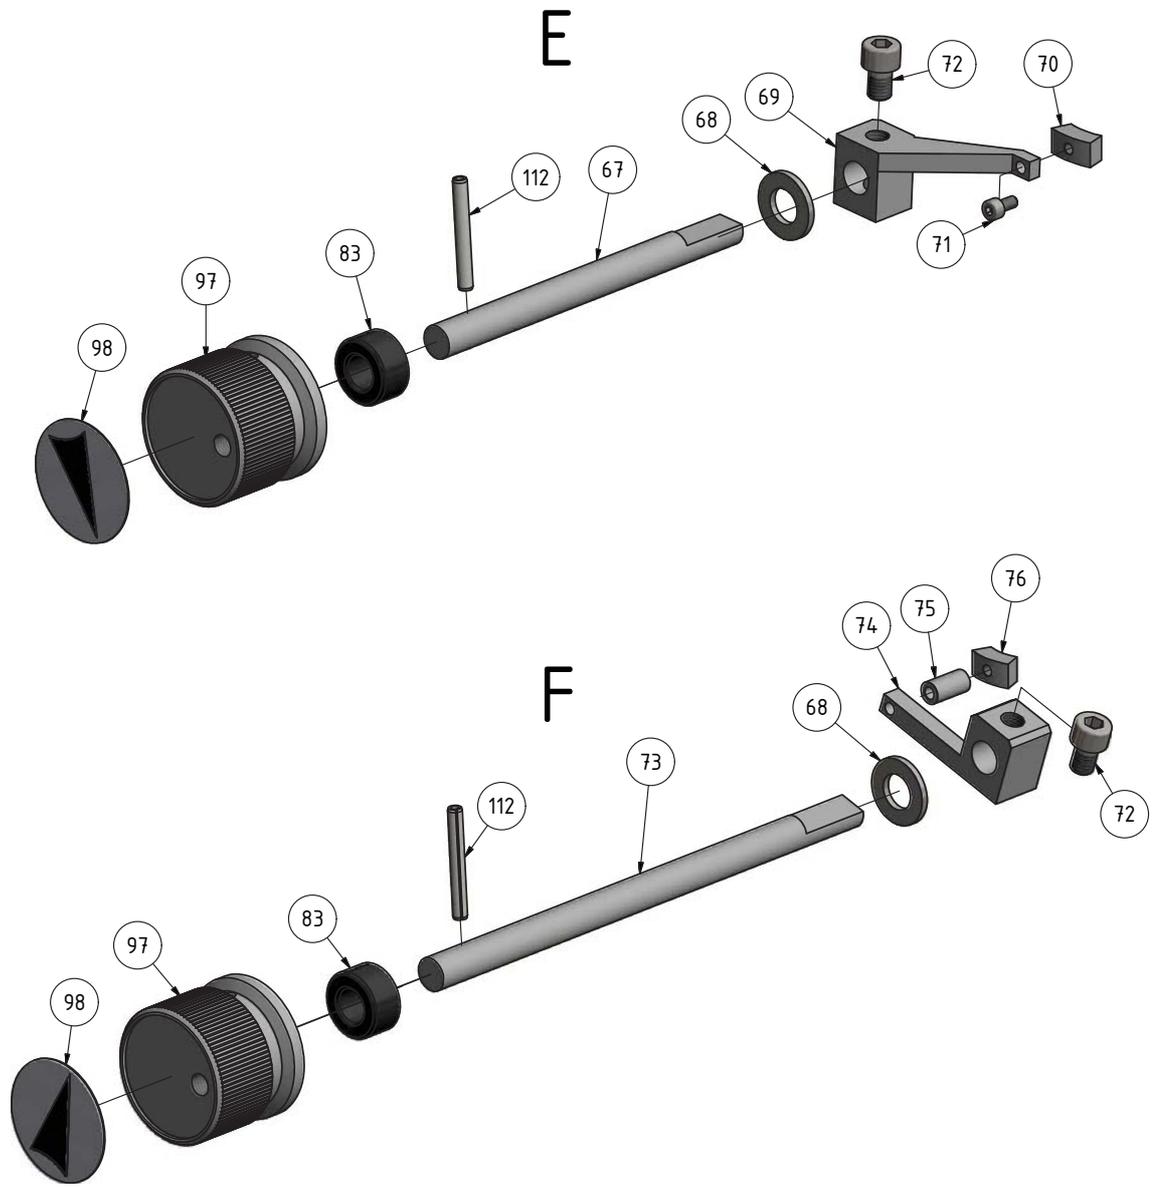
Fräskopf 4 von 6 - Milling head 4 von 6
